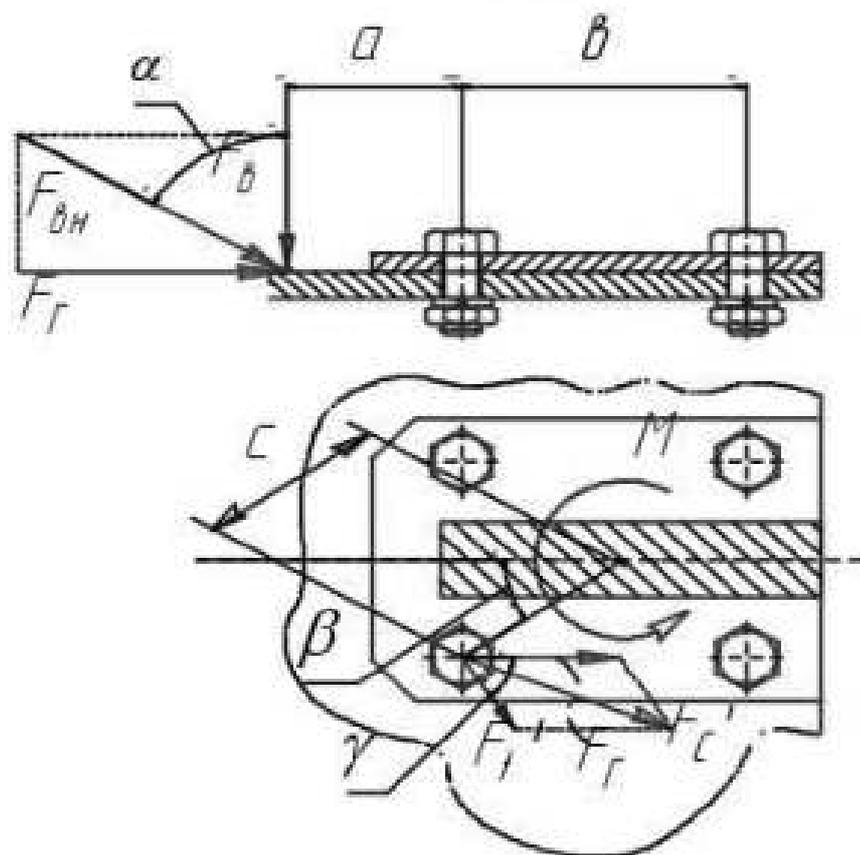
Схема к расчету болтов крепления стойки к лапе
